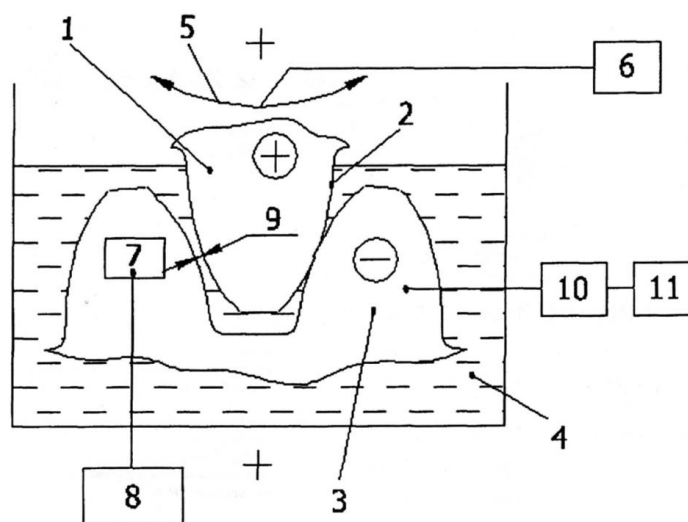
Схема способа восстановления профиля зубчатых колёс
